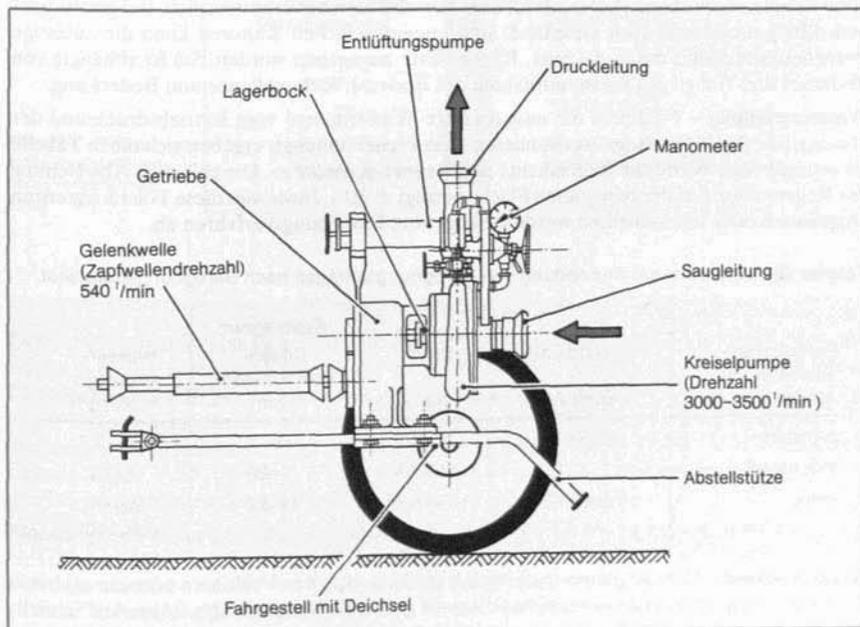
Aufbau einer zapfwellengetriebenen Pumpe für Beregnungsanlagen
